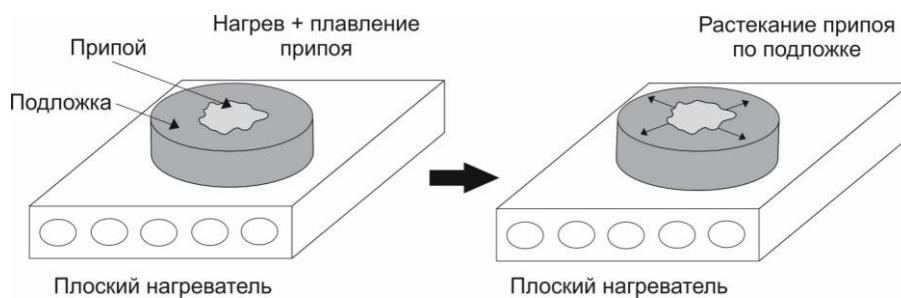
Схема нагрева подложки и нанесения припоя на поверхность алюминия
